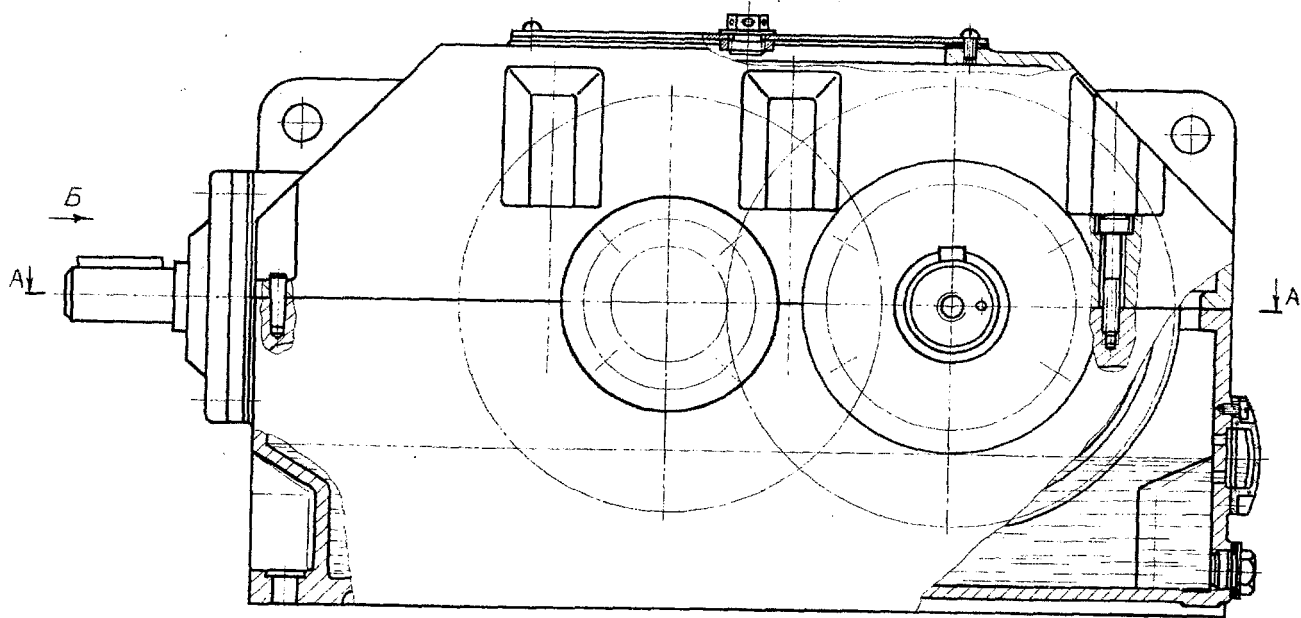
П. Редуктор коническо-цилиндрический двухступенчатый
